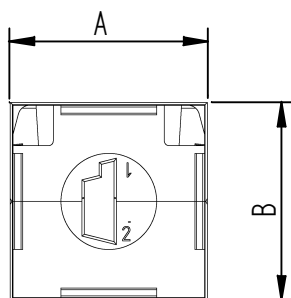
SKINTOP® CUBE MODULE ASI BUS
